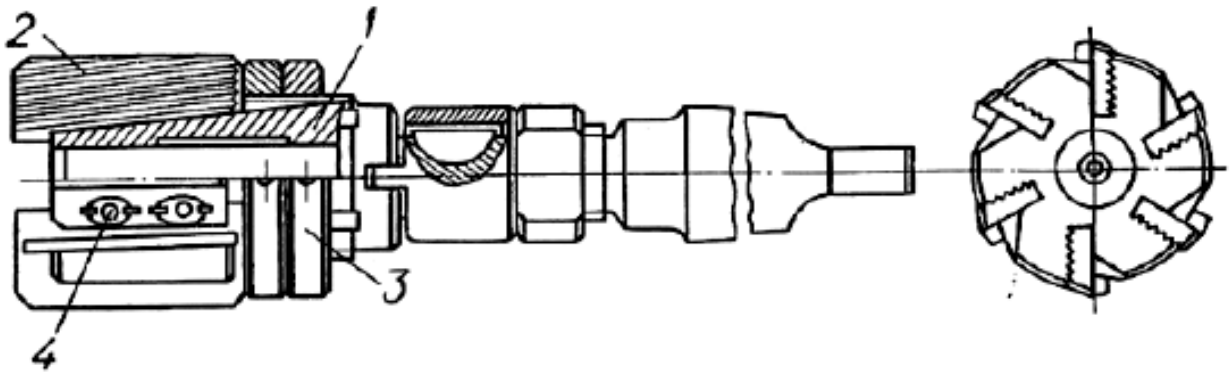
Розвертка 1 – корпус; 2 – вставні ножі; 3 – регулювальні кільця; 4 - болти
